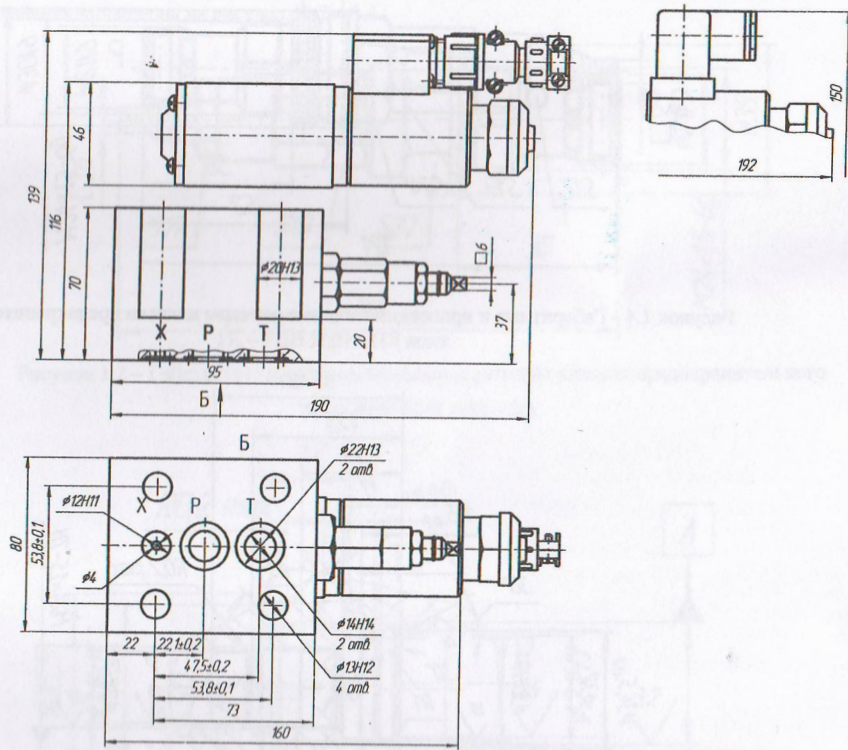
Габаритные и присоединительные размеры клапана предохранительного типа КПР 10/X CXX - XX
